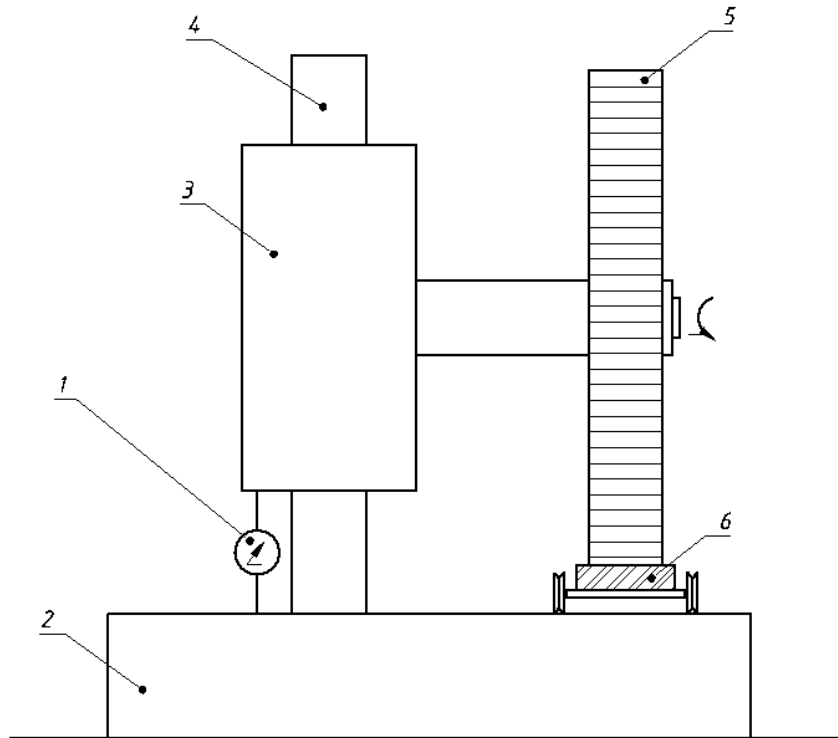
Схема вимірювання підймання-опускання пелюсткового шліфувального круга: 1 – індикатор годинникового типу; 2 – станина установки; 3 – супорт; 4 – направляючі; 5 – круг; 6 – зразок
